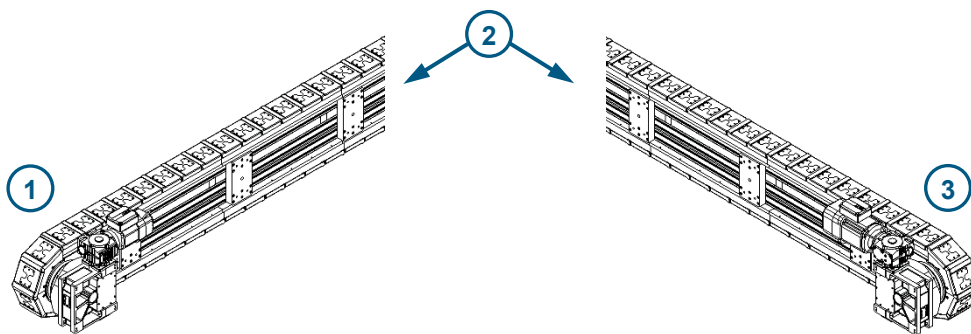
Posizioni di montaggio sistema di trasferimento lineare verticale
